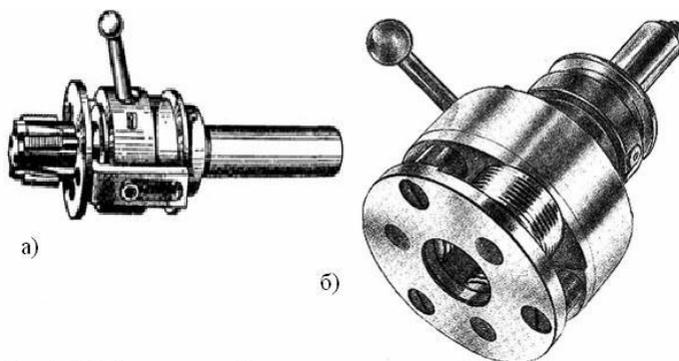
Головки резьбонакатные: *a* – для внутренней резьбы; *б* – для наружной резьбы
